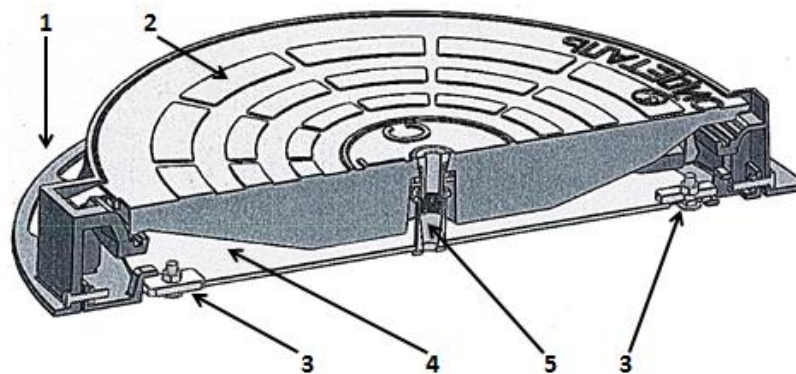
Разрез устройства УЗЛ-Т ССД с видом запорного механизма в закрытом положении: 1 - чугунная крышка; 2 – корпус люка; 3 – задвижки, зафиксированные в закрытом положении; 4 – нижняя стальная крышка; 5 – запорный механизм.
